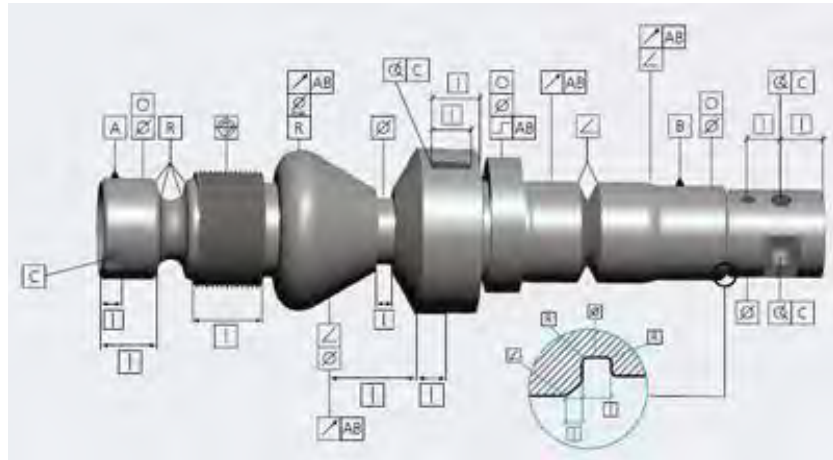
Forma isométrica de una pieza que muestra diferentes simbologías de tolerancia que pueden ser solicitadas para la fabricación de una pieza. (Hornel-Etamic, 2012).
